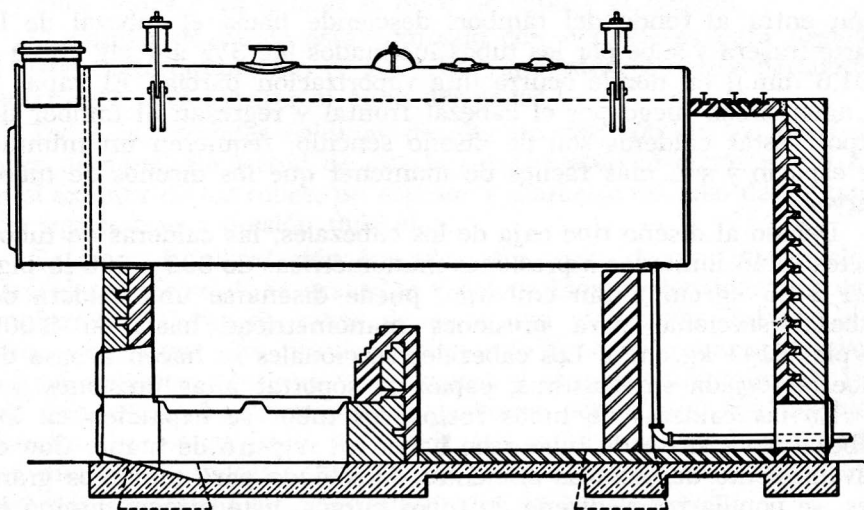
Caldera de tubos de humo. (Cortesía de Combustión Engineering-Superheater, Inc.)
